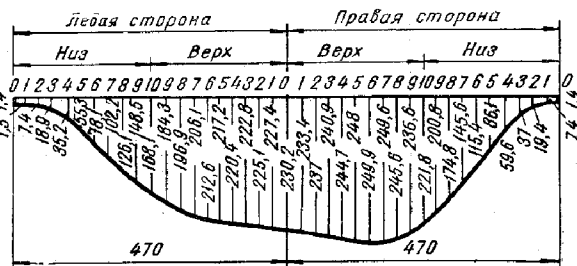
Развертка конца отростка сварного тройника.
